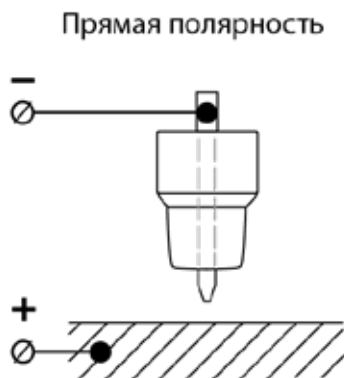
Полярность при TIG сварке.
